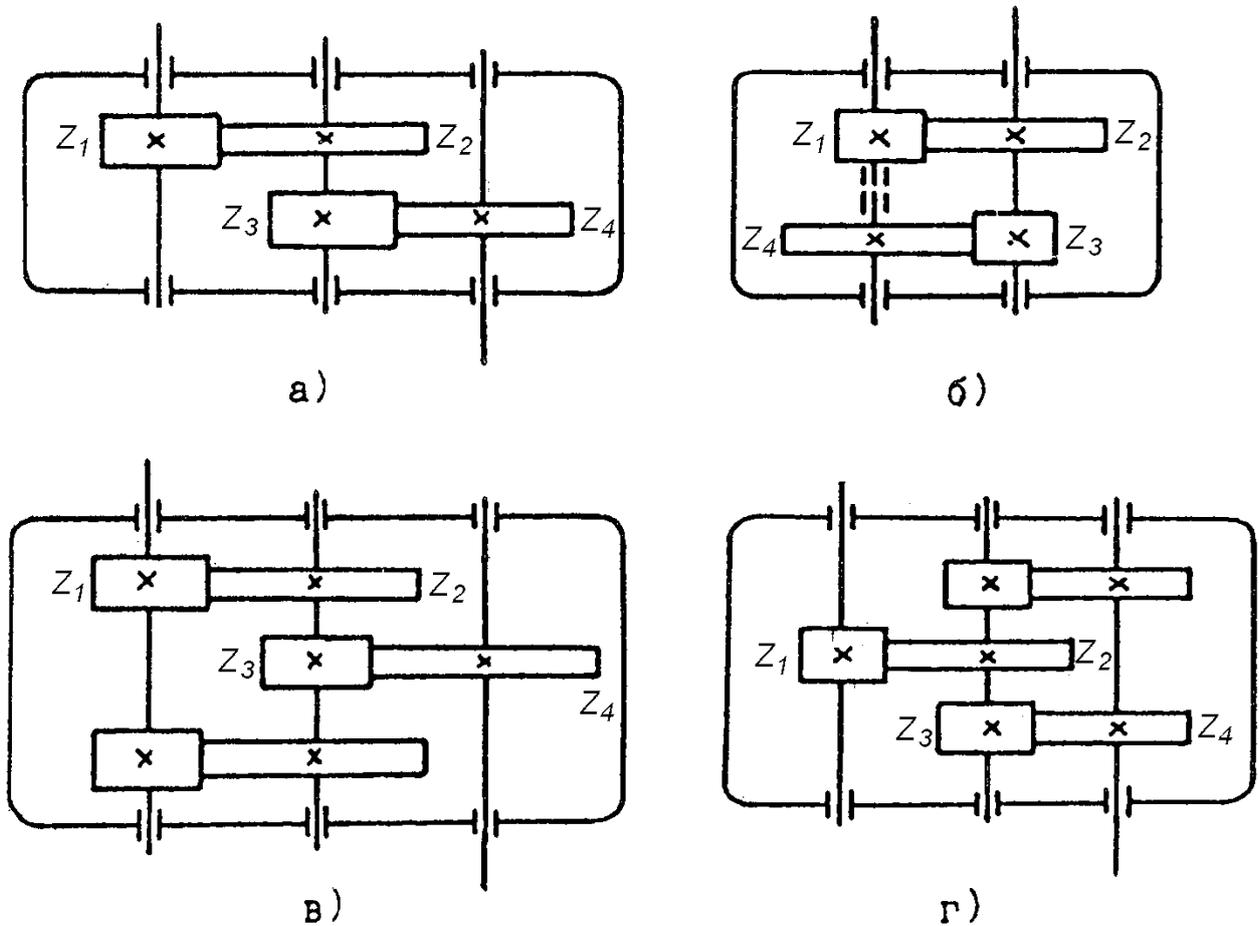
Кинематические схемы двухступенчатых цилиндрических редукторов
